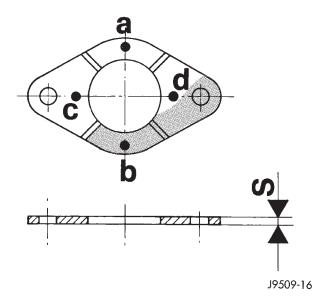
Placa de Montagem do Eixo de Comando de Válvulas
